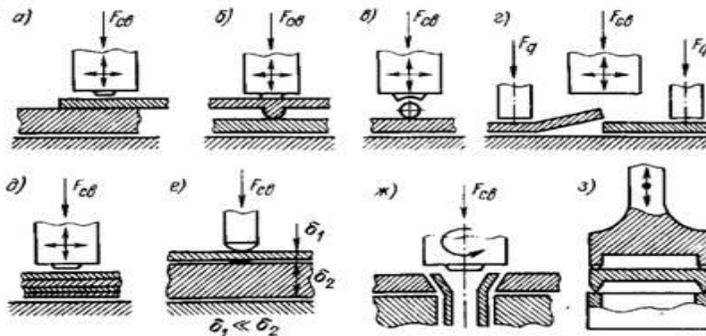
Основные типы сварных соединений металлов при УЗС [6]: а – внахлест; б – по профилю; в – параллельное соединение круглого и плоского профилей; г – с деформированием кромок; д – многослойных элементов; е – детали разной толщины; ж – угловое соединение; з – контурная сварка элементов. Стрелками показано направление колебаний сварочного наконечника.
